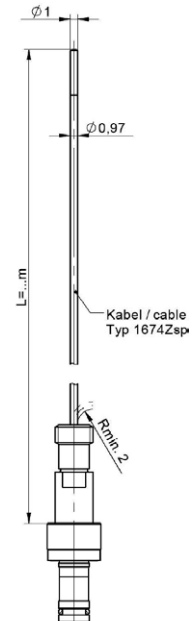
Sensor Typ 6177B mit Single-Wire Kabel und Krimpstift
